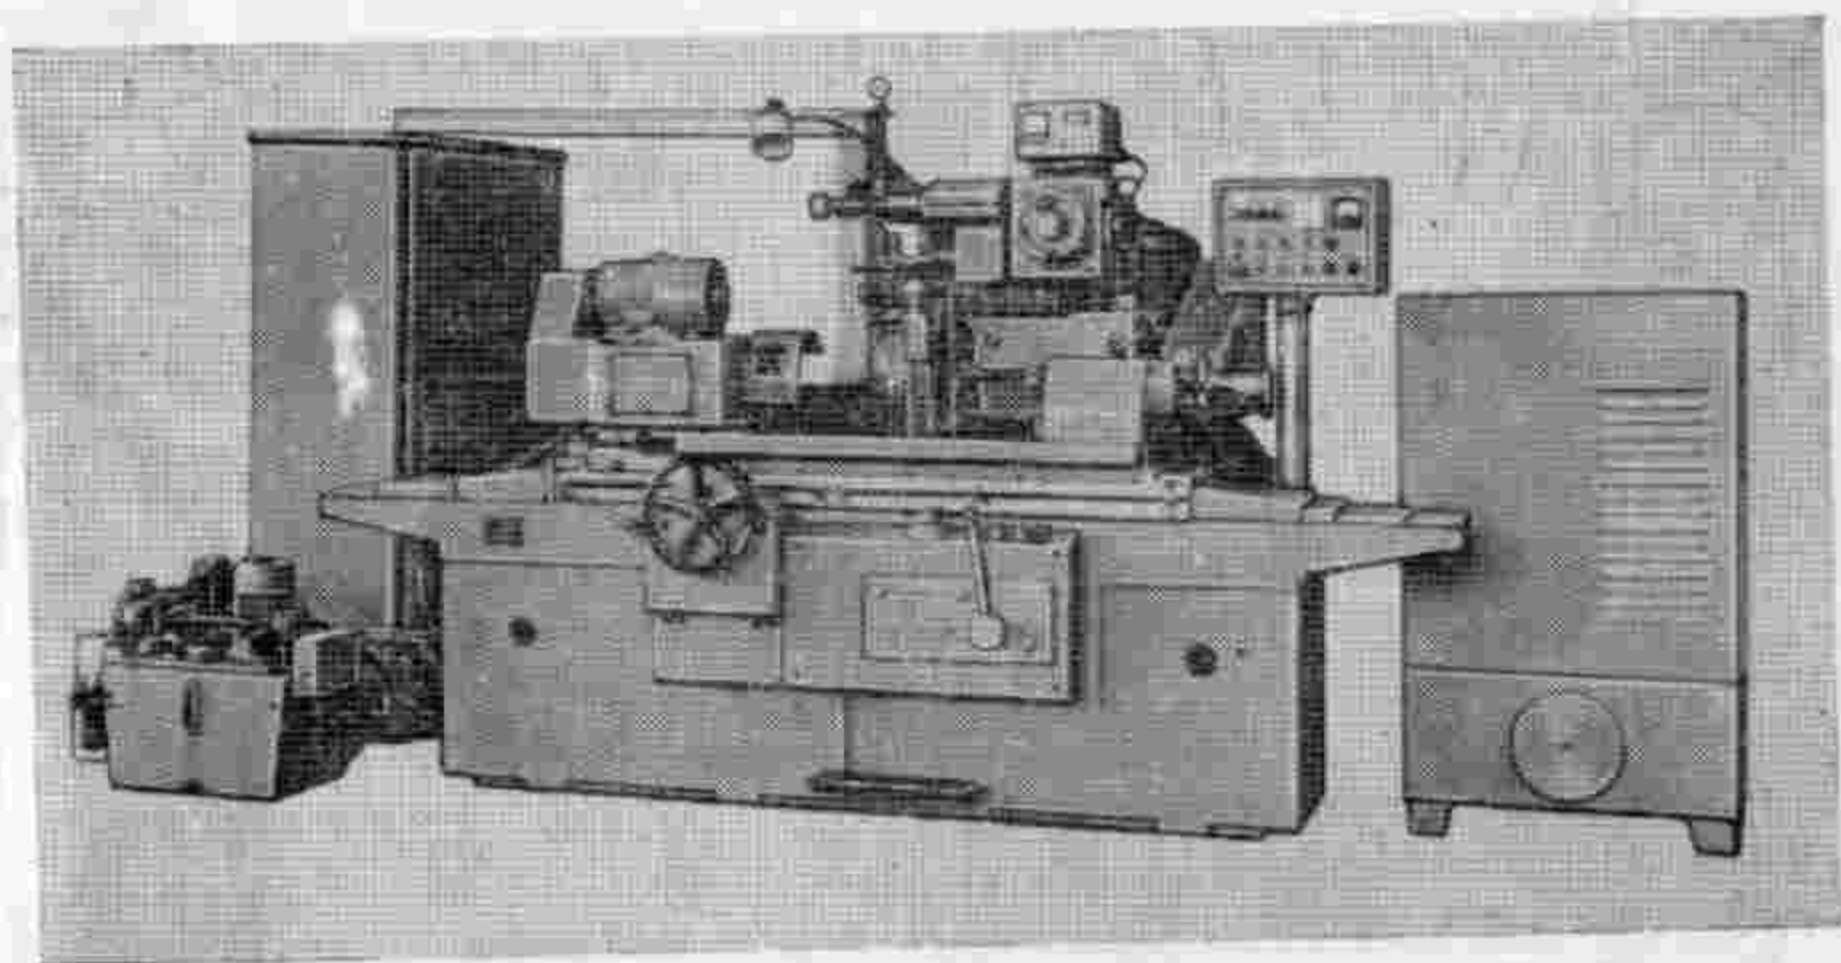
Станок круглошлифовальный универсальный ЗУ131ВМ
